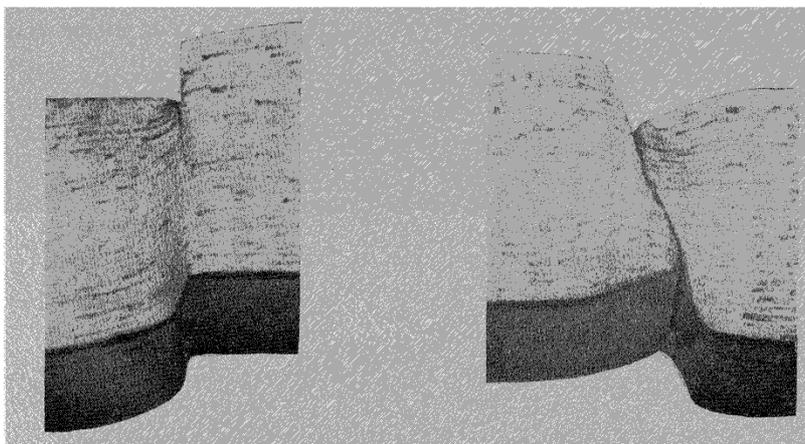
et 91. — Cisaillement d'une éprouvette d'acier, de 8 mm d'épaisseur, maintenue par une butée de levage; et cisaillement de la même éprouvette libre de s'incliner.
